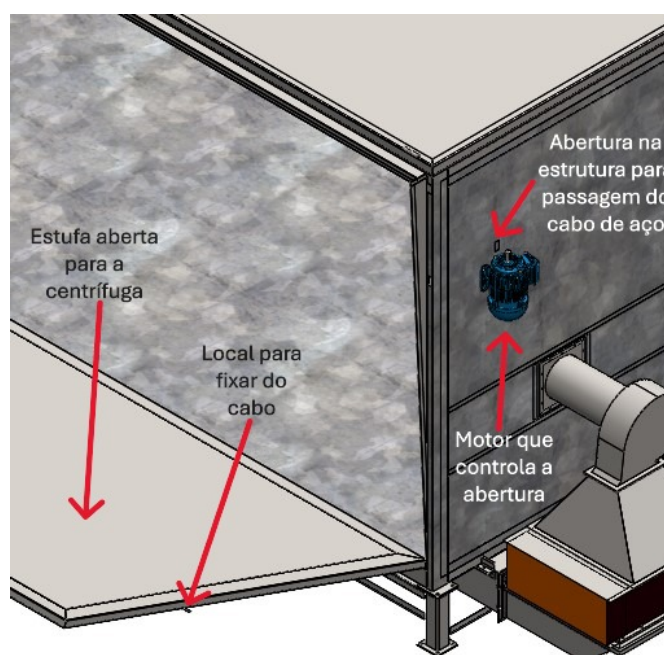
Acionamento de abertura da estufa para a centrífuga do lado 2.
